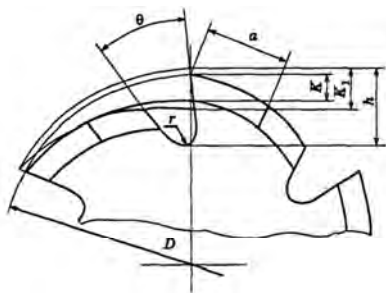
Элементы профиля зуба и впадины резьбовой фрезы
